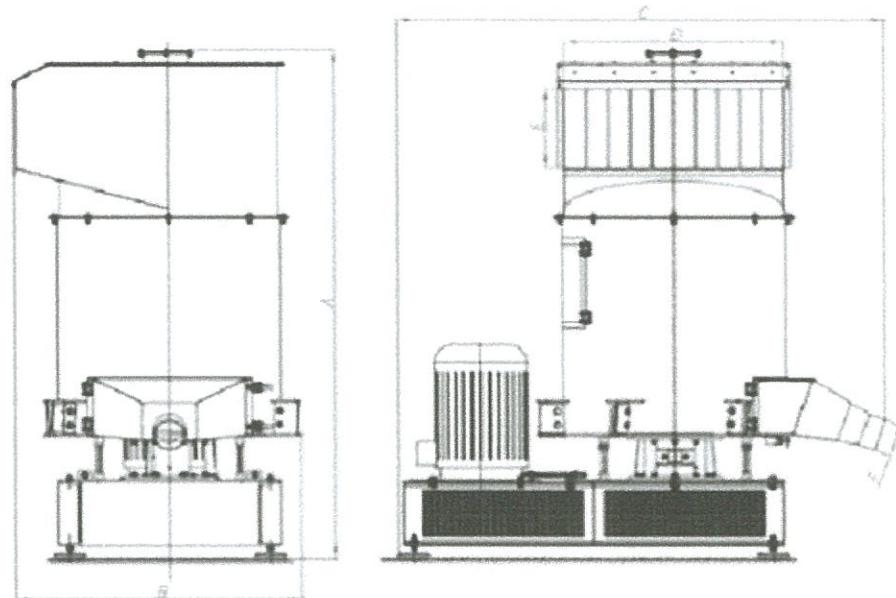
Дробарка з вертикальною віссю обертання ротора
